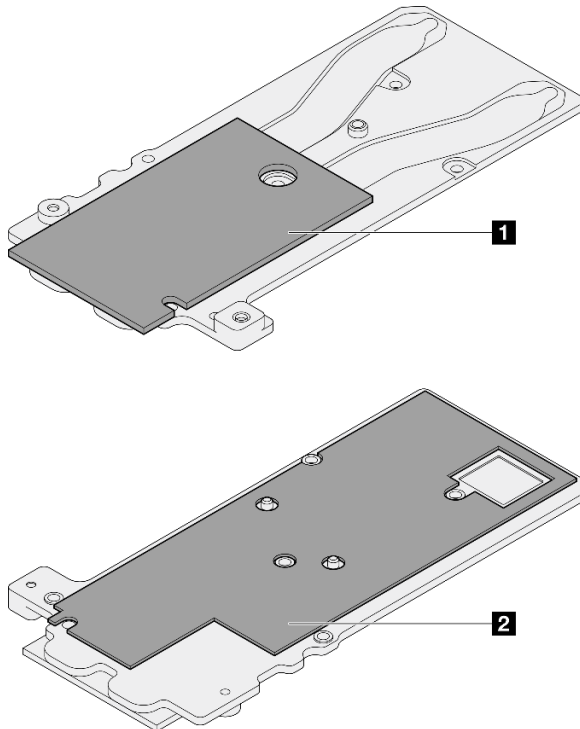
Remplacement des tampons de mastic de la plaque de conduction du module OSFP
